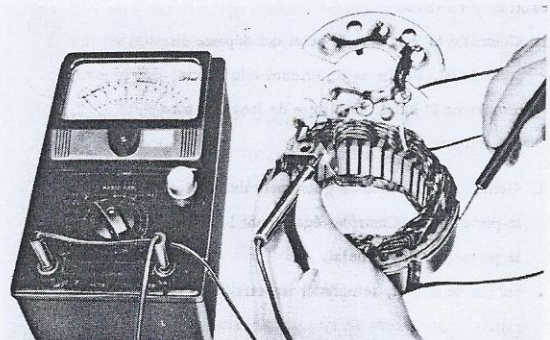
Contrôle de mise à la masse du bobinage de stator.
